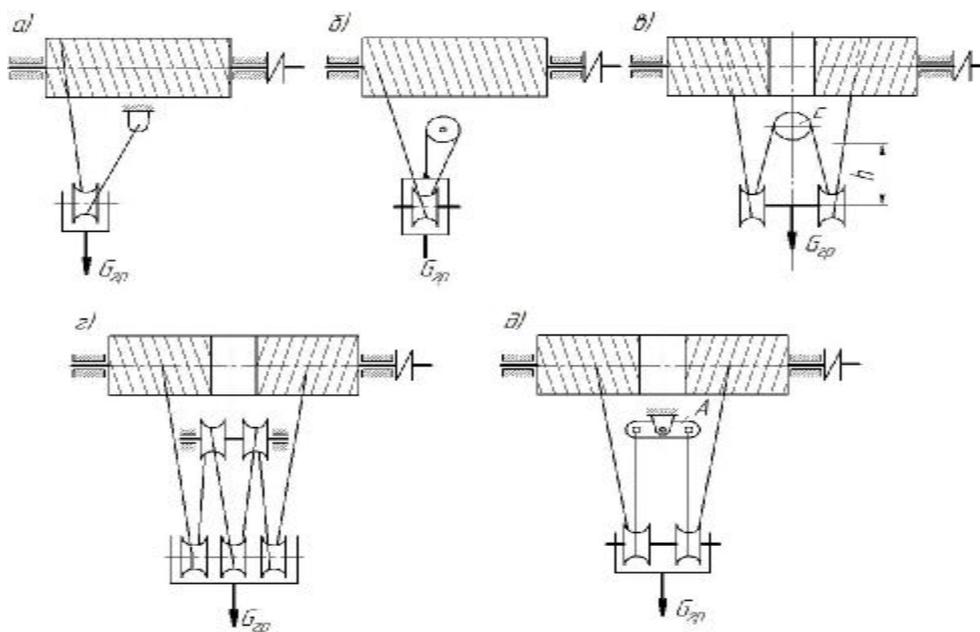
Барабаны с нарезанными винтовыми канавками
